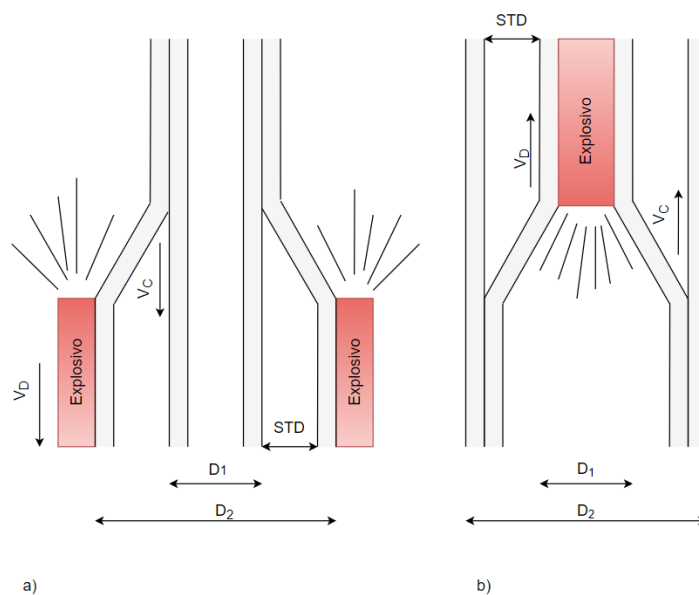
Esquematização em corte da configuração cilíndrica do processo soldadura por explosão, com (a) O explosivo colocado por fora do cilindro de maior diâmetro; (b) O explosivo colocado por dentro do cilindro de menor diâmetro.
